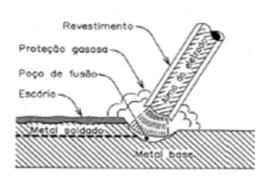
Ilustração de um processo de soldagem por eletrodos revestidos – SMAW. Fonte: Apostila do Cursos de Inspetor de Soldagem N1 - CETRE (2003).
